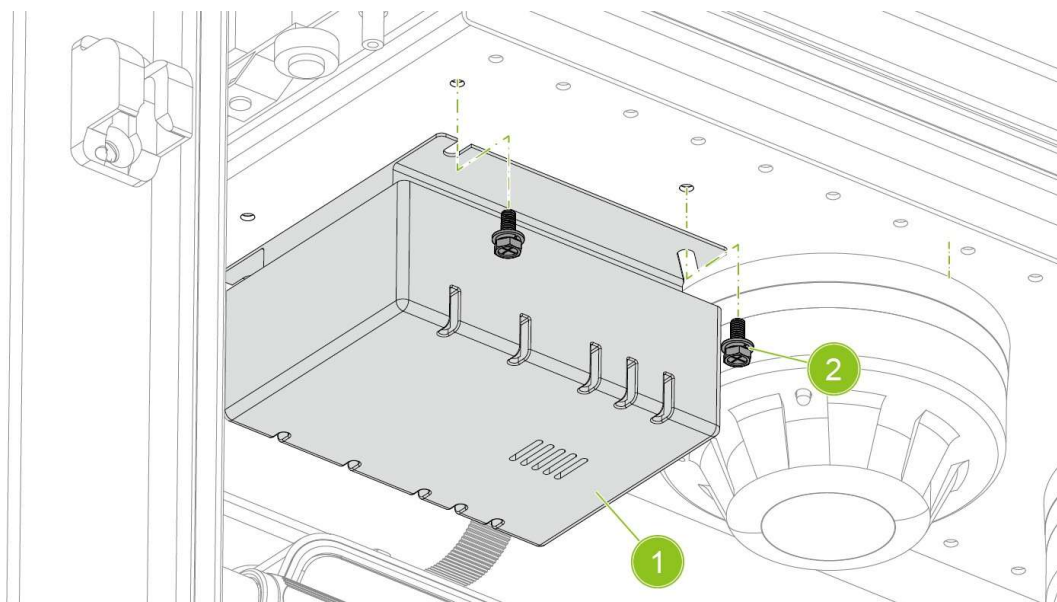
Remova os parafusos de fixação do detector de gás combustível
